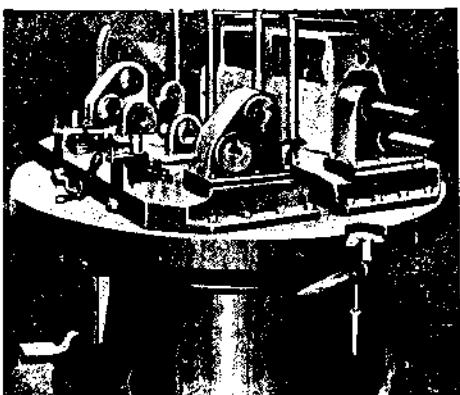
Двойное приспособление для расточки с люнетами, имеющими прорези для пропуска резцов.
